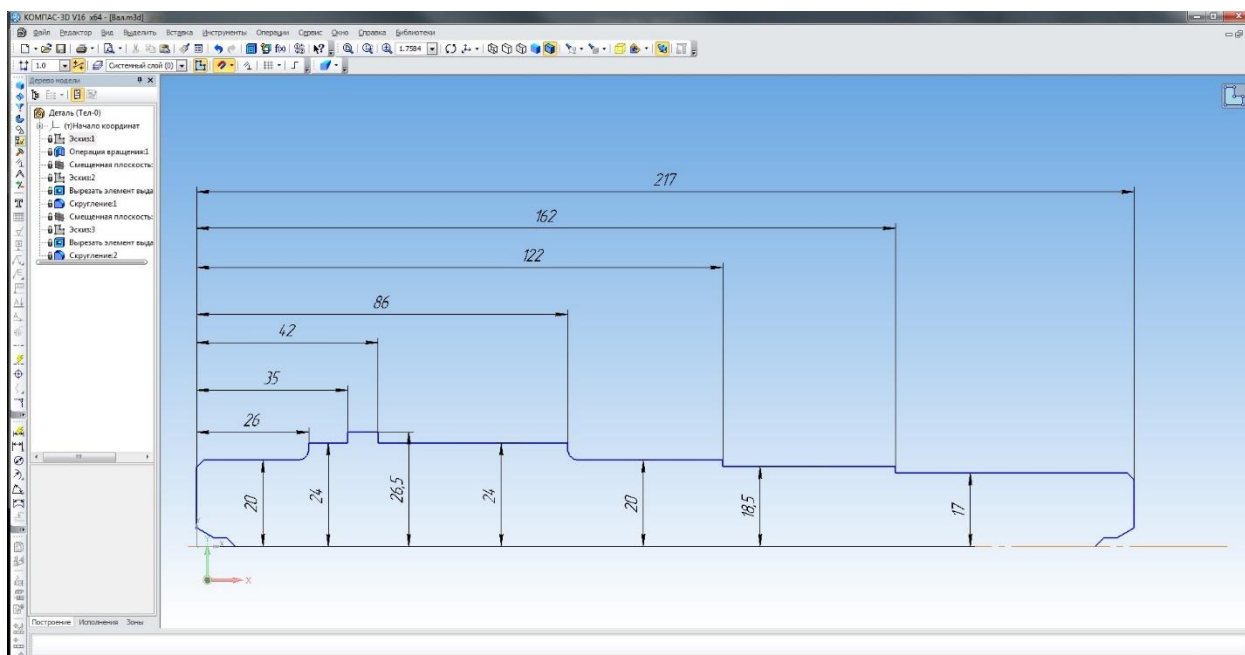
Ескіз 1 деталі «Вал тихохідний» з розмірами для операції обертання
